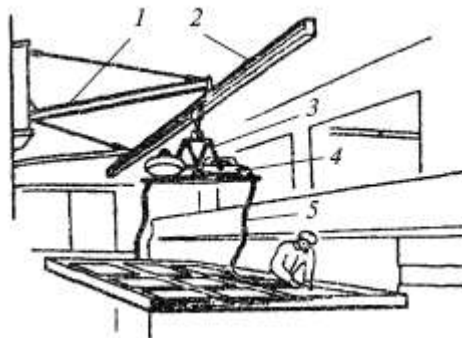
Стационарная установка для механизированной сварки крупногабаритных изделий:
